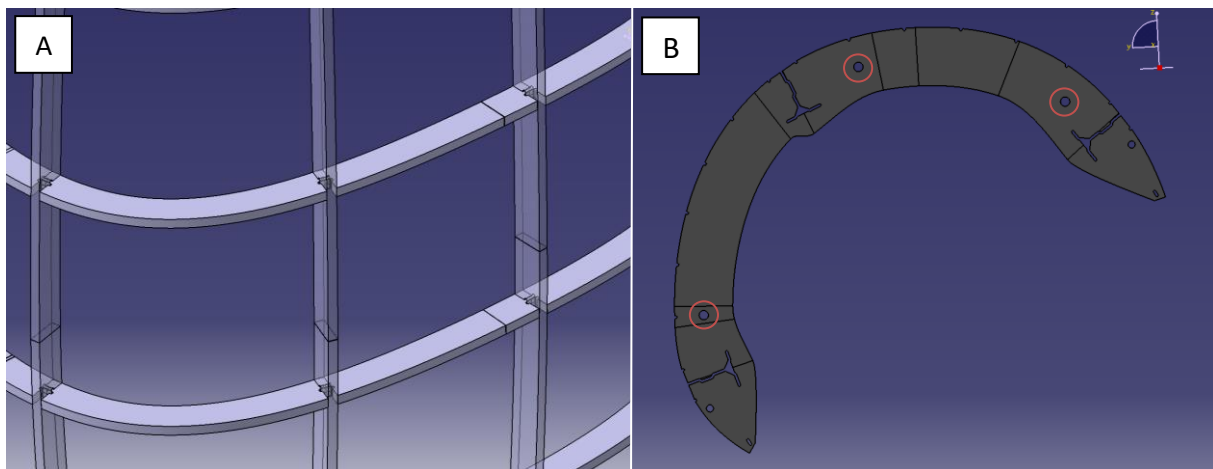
Bild A: Ausschnitte der Spanten und der Stringer; Bild B: Ausschnitte im hinteren Hauptspant, Bohrungen für den Anschluss an den Hauptspanträger ro markiert.
